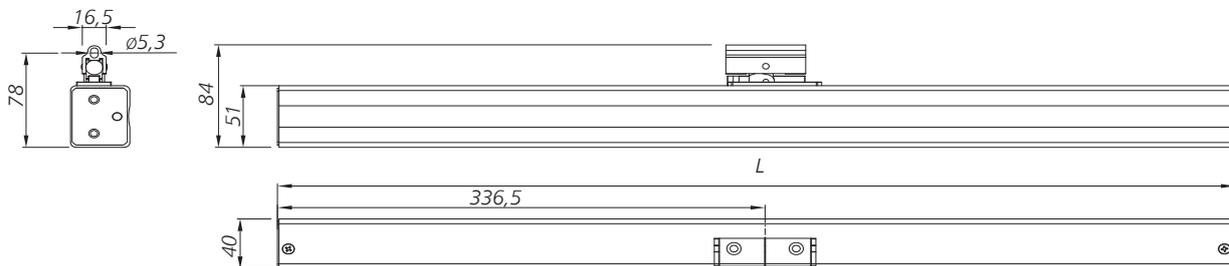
Abmessungen des Kettenträgers HCVA, Abmessungen [mm]
